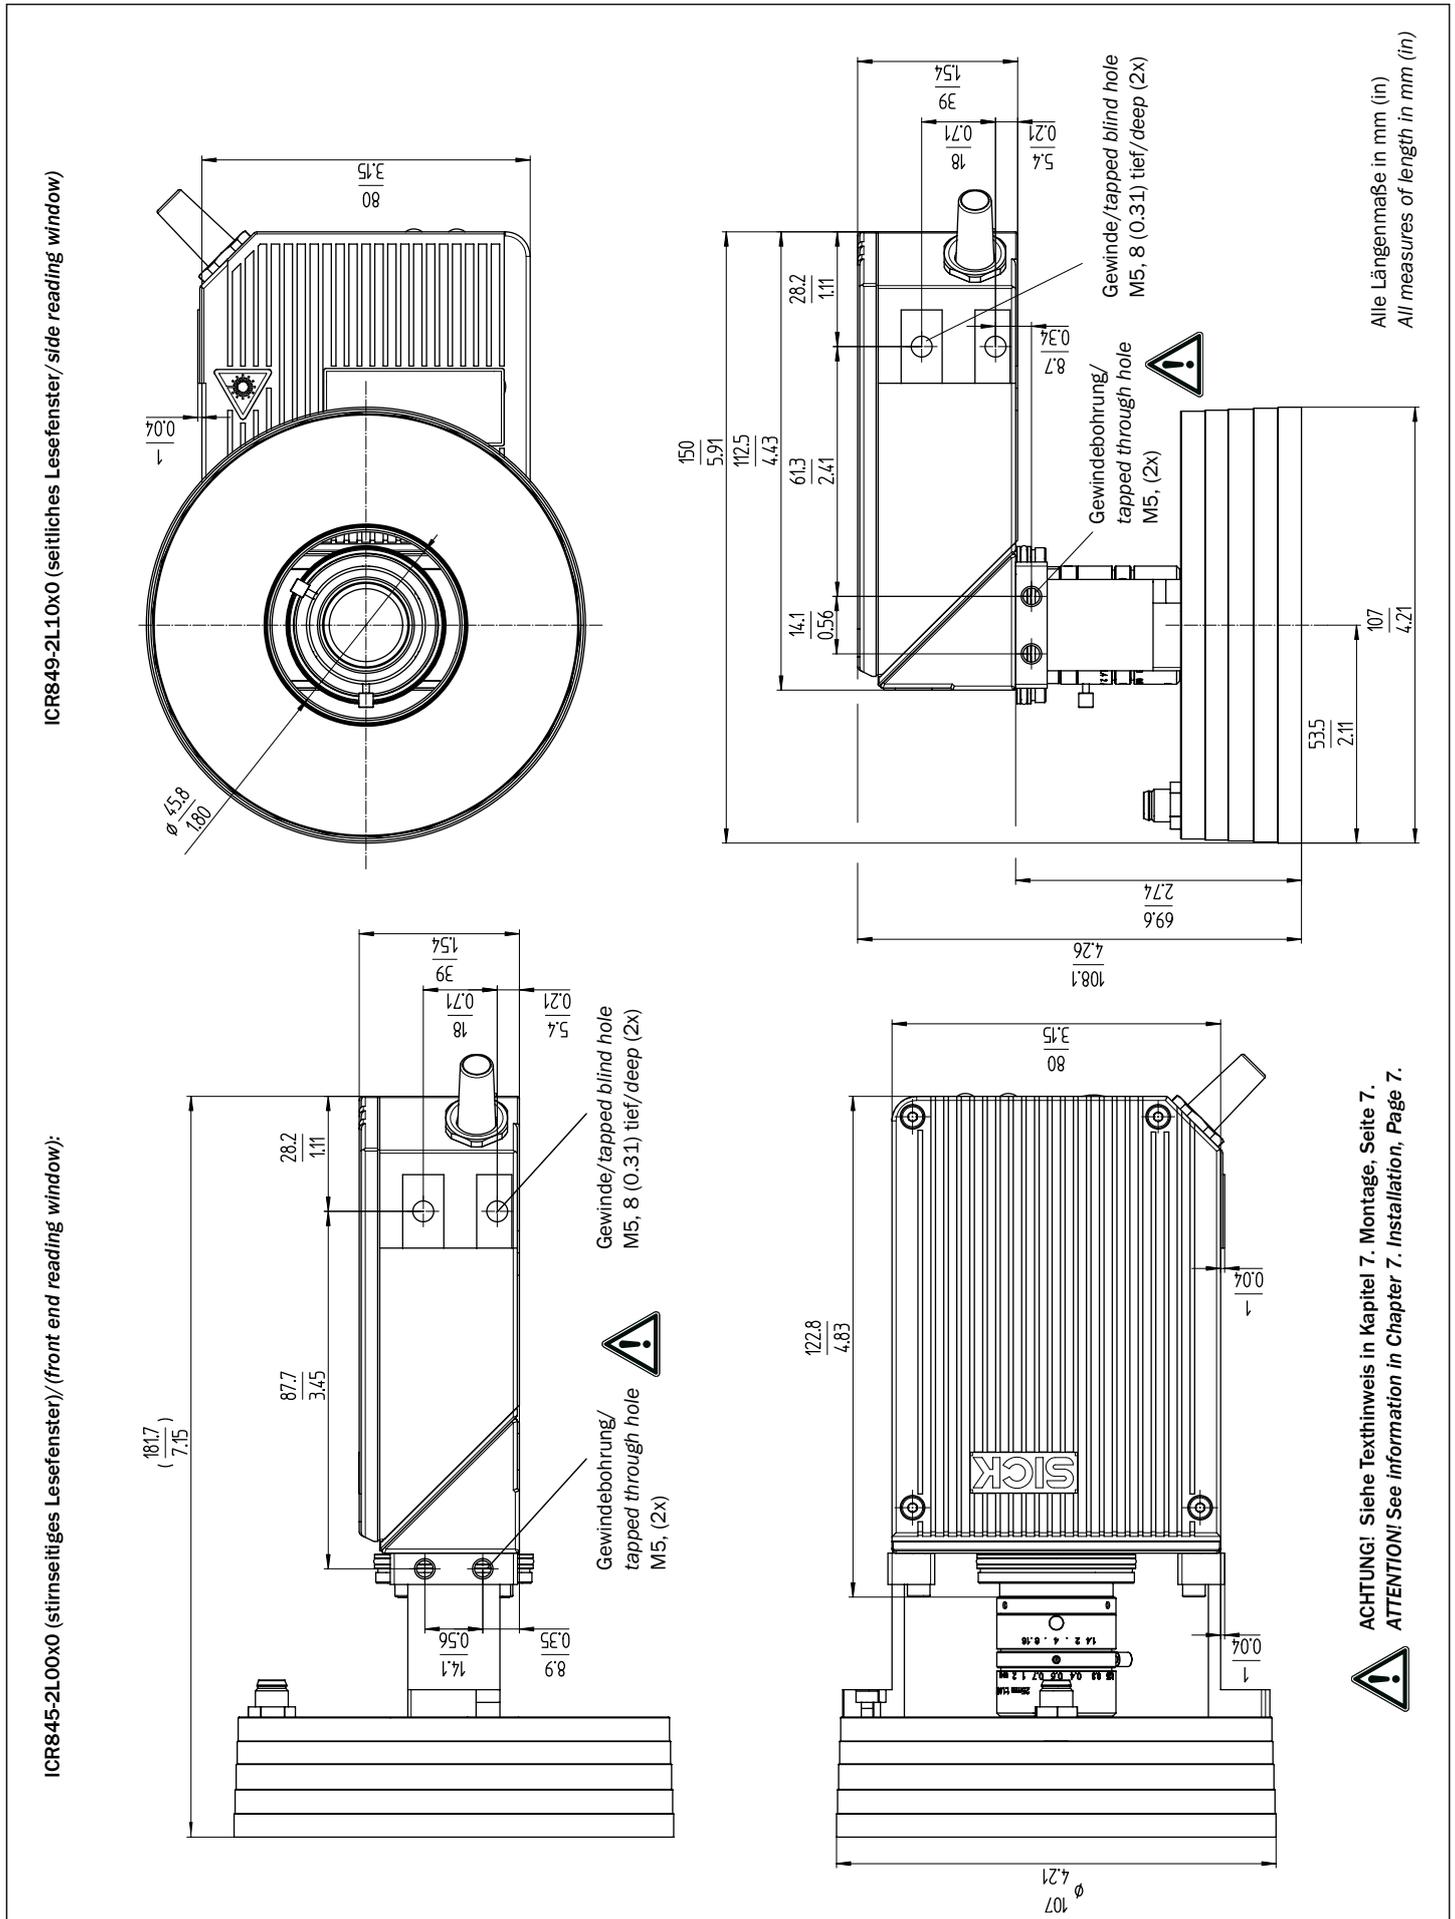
ICR84x-2L00x0/-2L10x0 FlexLens: Abmessungen mit montierter Ringbeleuchtung ICL170, ICL260, ICL280 oder ICL300
